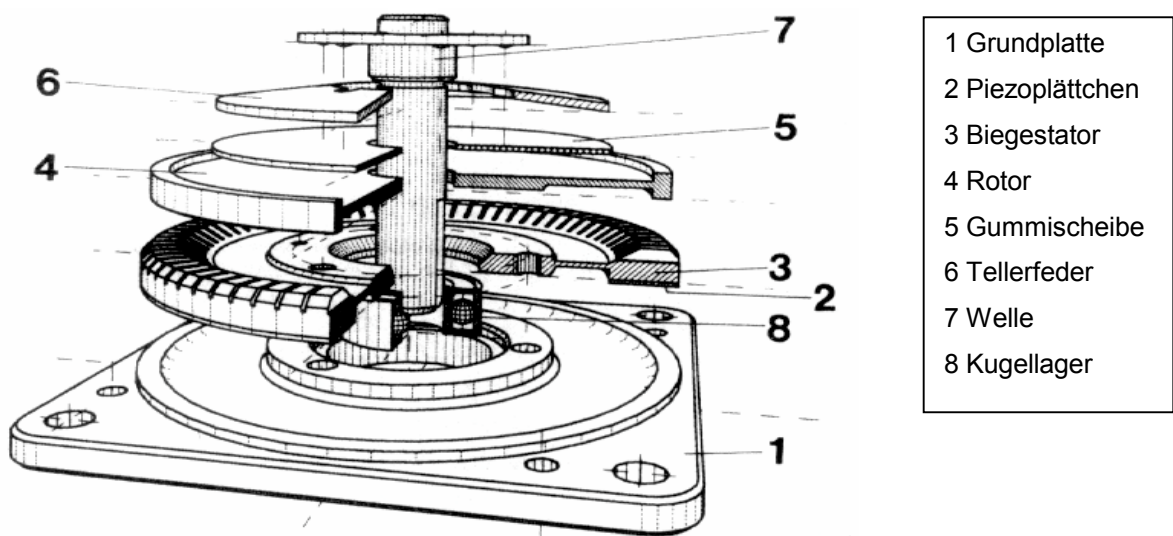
Explosionszeichnung eines Shinsei-Wanderwellenmotors, hier: USR-60
